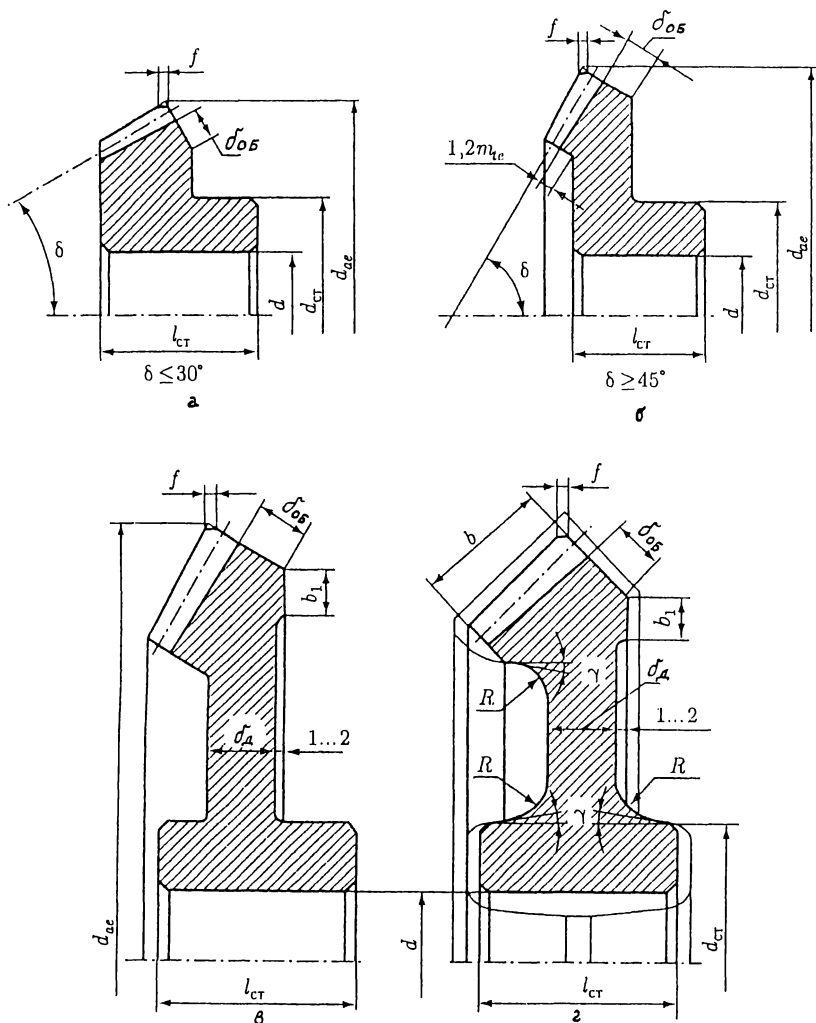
Формы конических зубчатых колес [3]:
